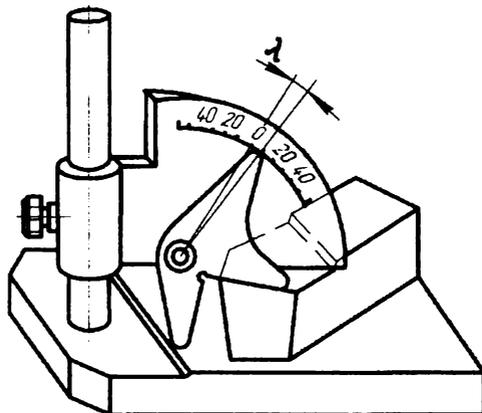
Схема измерения угла λ токарного проходного резца
